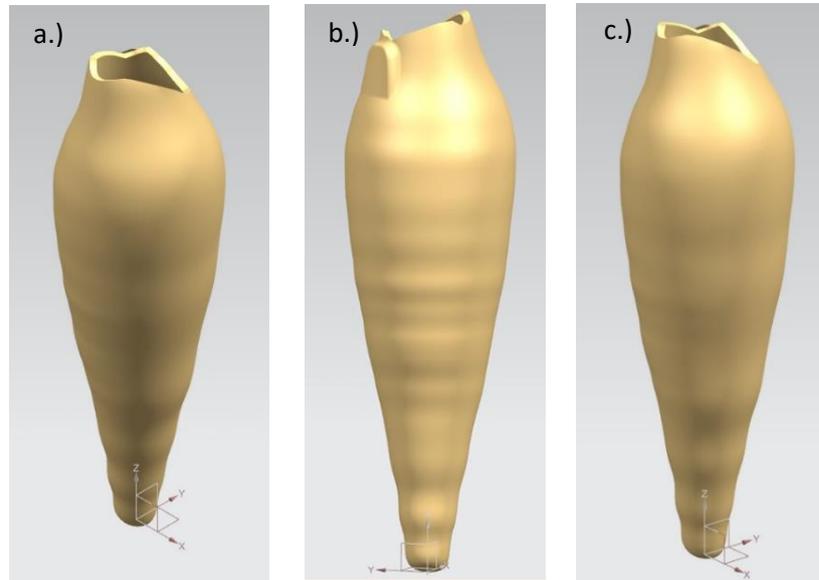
(a-b-c) a.) Vista lateral en plano picado. b-) Vista del lateral izquierdo en alzado del modelo 3D finalizado. c.) Vista de lateral derecho en alzado del modelo 3D finalizado.
